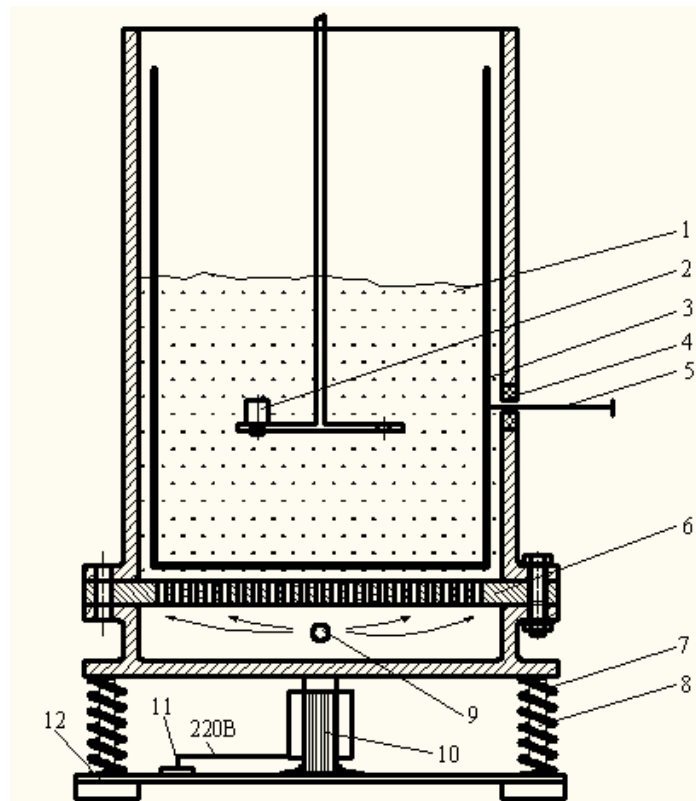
Установка для нанесення полімерних покриттів на металічні поверхні в іонізованому псевдо зрідженому стані: 1 – псевдозріджений шар; 2 – зразок; 3 – електрод; 4 – прохідний ізолятор; 5 – шина високої напруги; 6 – пориста перегородка; 7 – пружина; 8 – направляюча; 9 – отвір для подачі повітря; 10 – електровібратор; 11 – клемник; 12 – станина.
